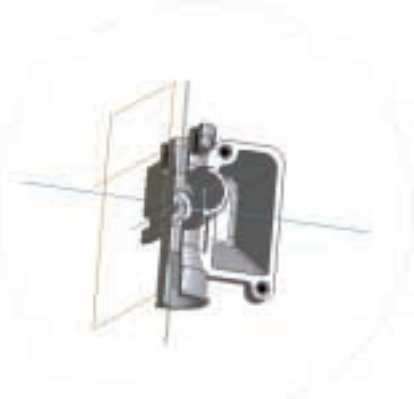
Корпус карбюратора K38, полученный модификацией корпуса K68
